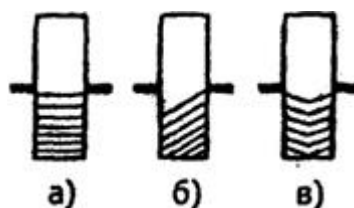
Условные обозначения зубчатых колес с прямыми (а), косыми (б) и шевронными (в) зубьями
